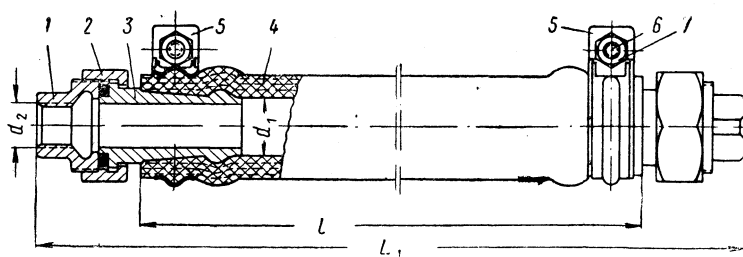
Рукав соединительный типа Р3 ГОСТ 2593—55
